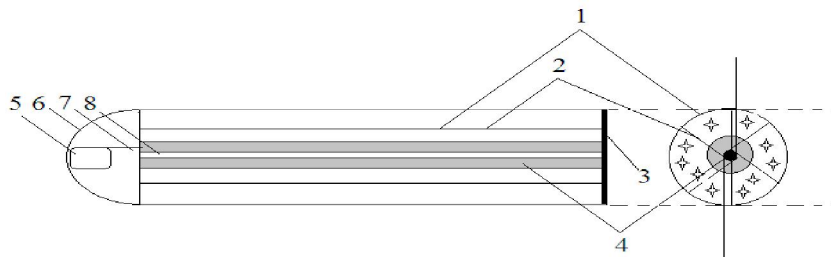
Модель контейнера з порошковою вогнегасною речовиною: 1 – корпус; 2 – розділювач секцій; 3 – задня торцева частина контейнера; 4 – спонукальний пристрій; 5 – механізм приведення в дію спонукального пристрою; 6 – лобова частина; 7 – запальник механізму; 8 – центральна вісь корпусу
